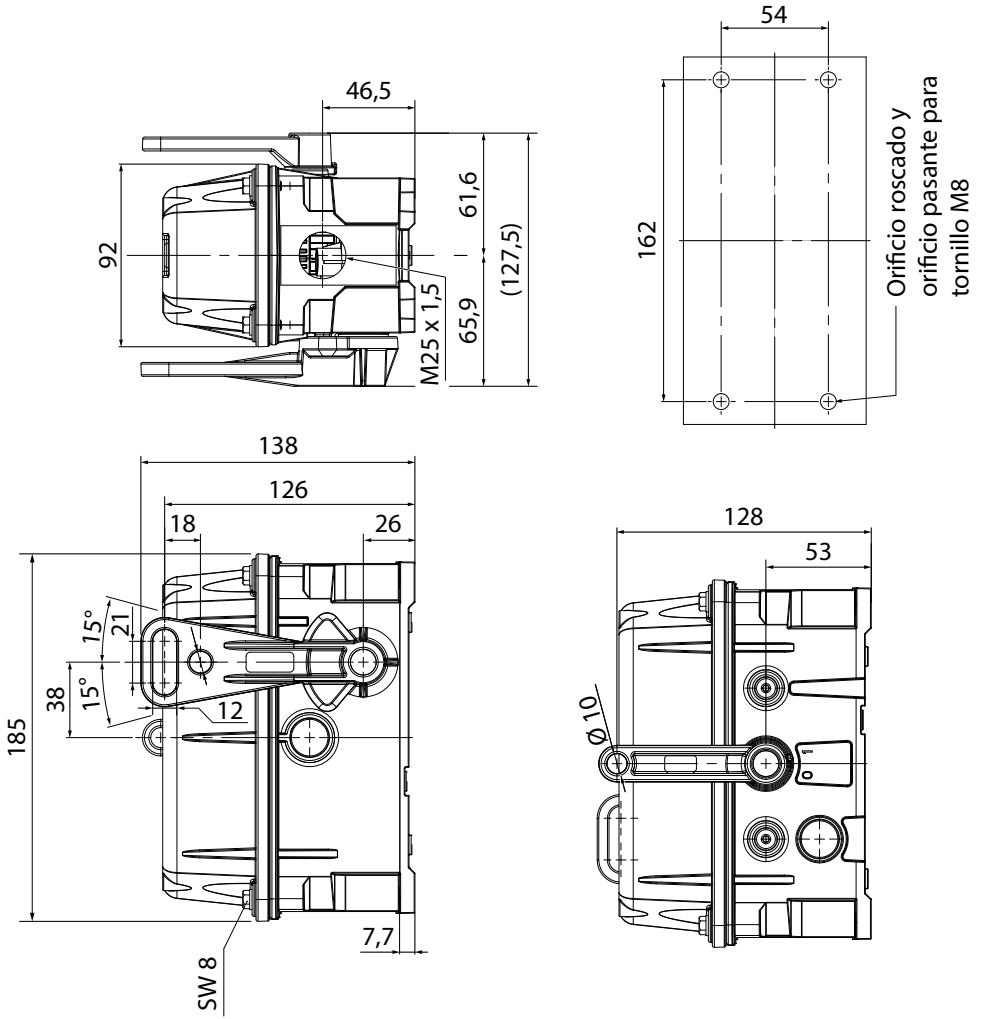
Planos de dimensiones (dimensiones en mm)
